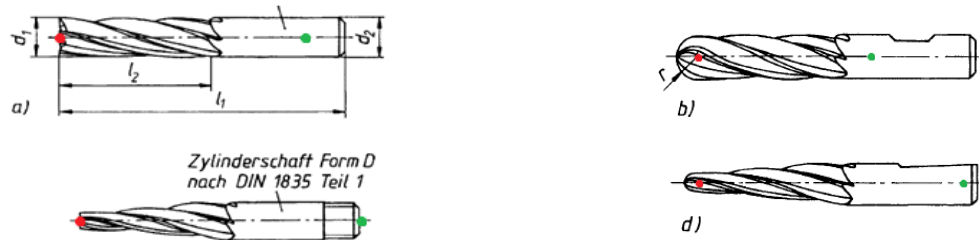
Schaftfräser in kegeliger und zylindrischer Ausführung [PHL08]
